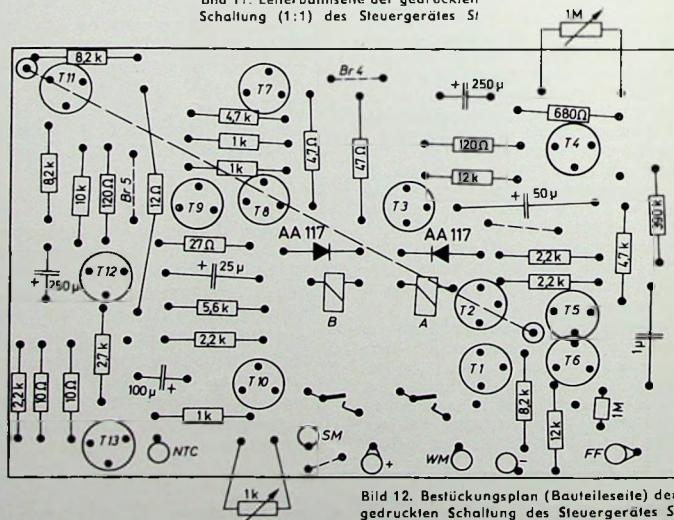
Bestückungsplan (Bauteileseite) der gedruckten Schaltung des Steuergerätes SI
